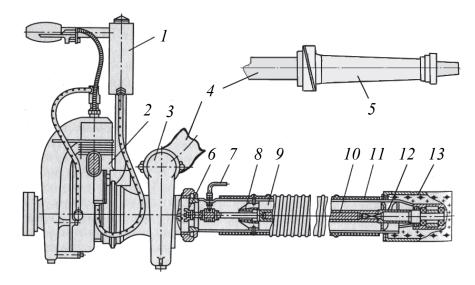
Лесопожарная мотопомпа МЛН-3,0/0,35У1: 1 — рама-бак; 2 — двигатель внутреннего сгорания; 3 — центробежный насос; 4 — напорный рукав; 5 — пожарный ствол РС-504; 6 — кулачковая муфта; 7 — ручка-переключатель; 8 — пружина; 9 — полость рукава; 10 — гибкий вал; 11 — водозаборный рукав; 12 — осевой насос; 13 — фильтр
